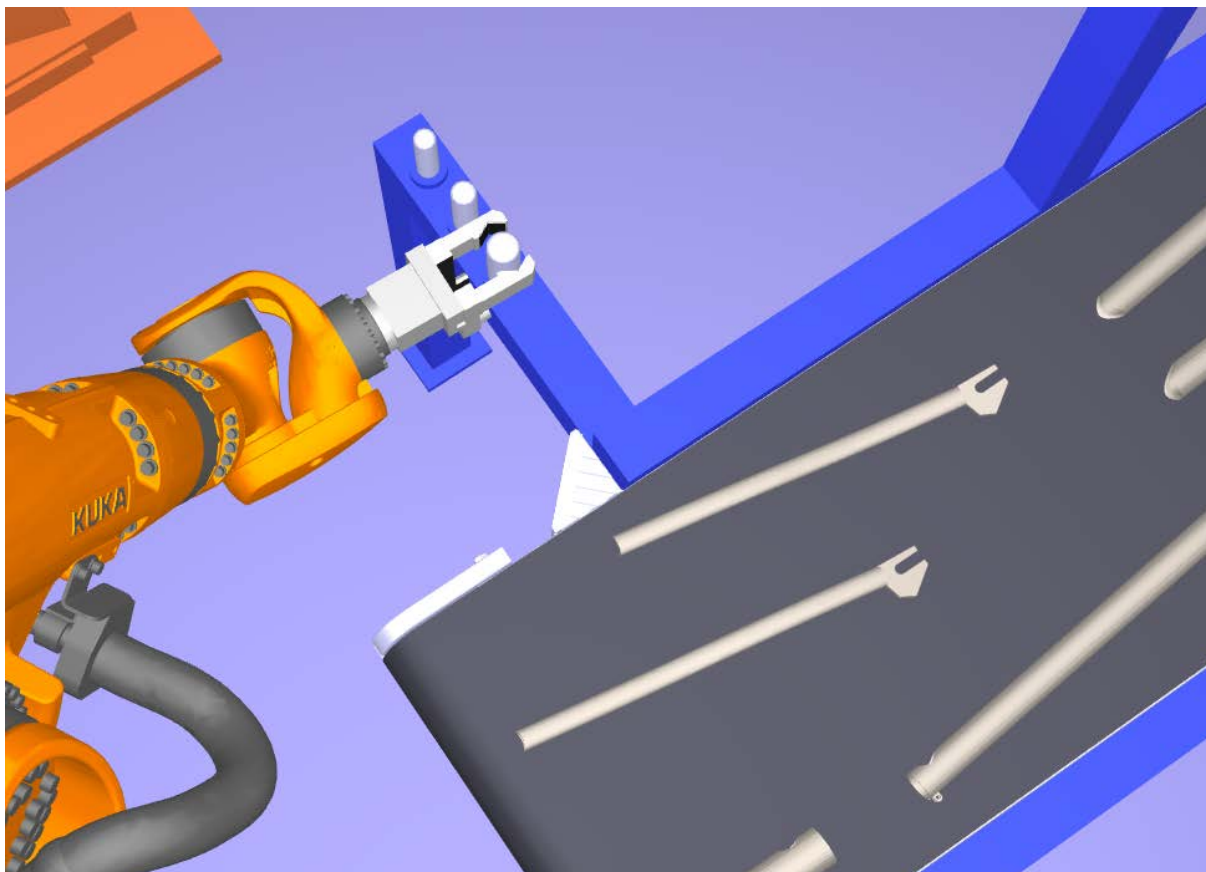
Використання захвату роботом KUKA KR 16 R1610 для складання та зварювання рами
